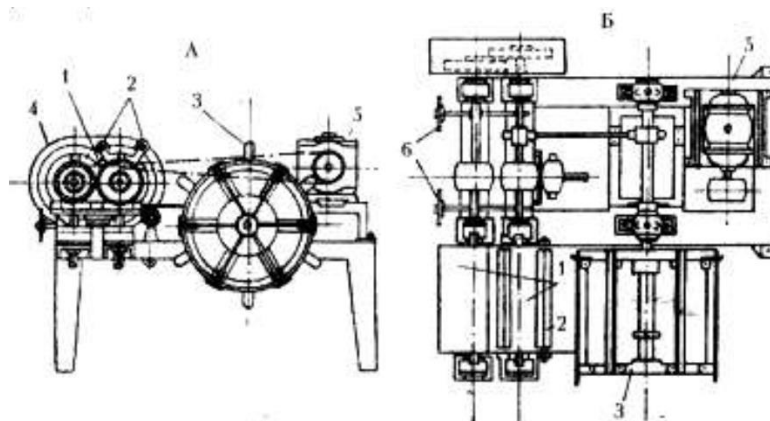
Щіткова кисть (А - вид збоку, Б - вид зверху.) 1 – циліндричні щітки; 2 – напрямні валики; 3 – моталка; 4 – кожух; 5 – електродвигун; 6 – регулювальні гвинти.
